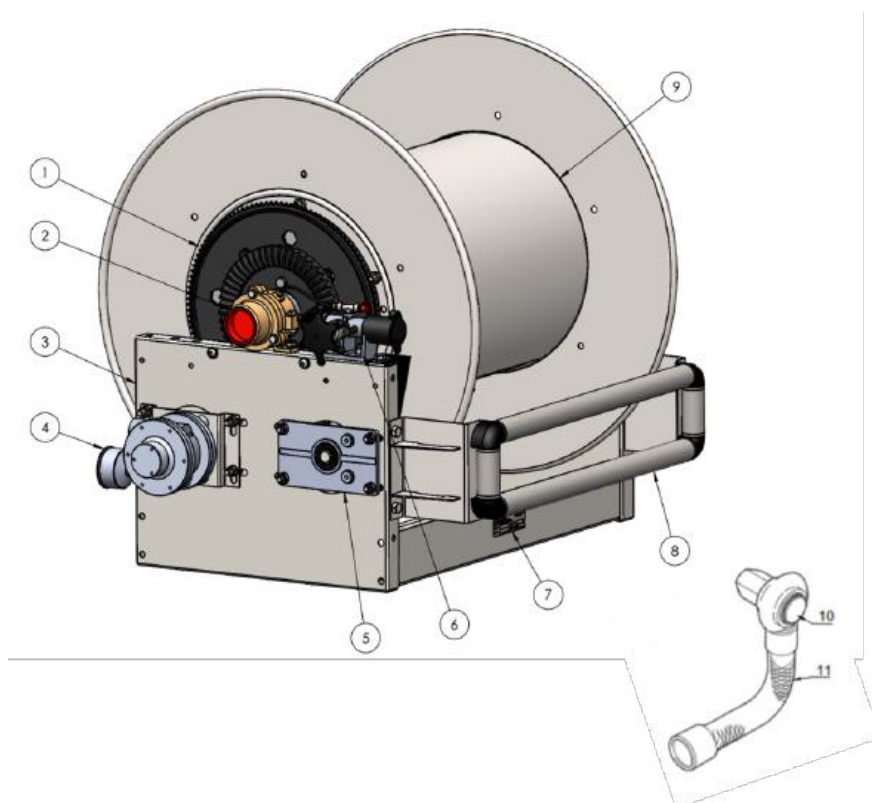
Enrollador de manguera de rebobinado con motor neumático (Protector de cadena desmontado)
